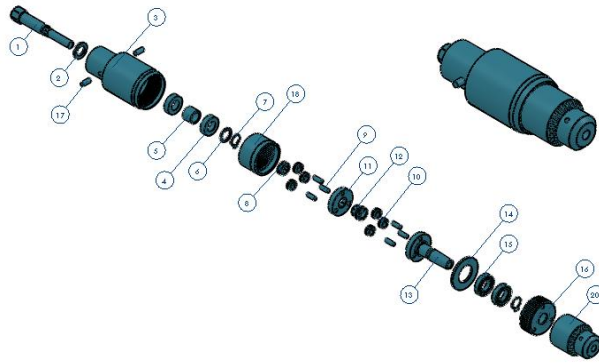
Vista explosionada del ensamble del modulo de taladro
